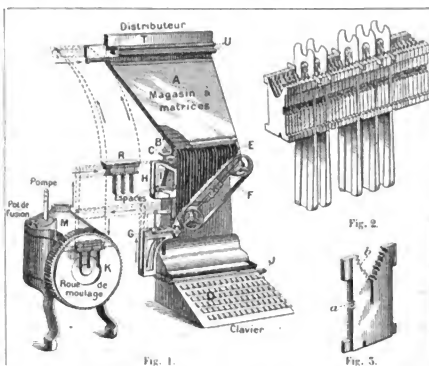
, 2 et 3. La linotype, machine à composer. — Fig. 1. Principe de fonctionnement de la machine. — Fig. 2. Matrices disposées pour former le moule d'une ligne de composition. — Fig. 3. Matrices servant à former les moules (32 millimètres de hauteur sur 19 millimètres de largeur).
